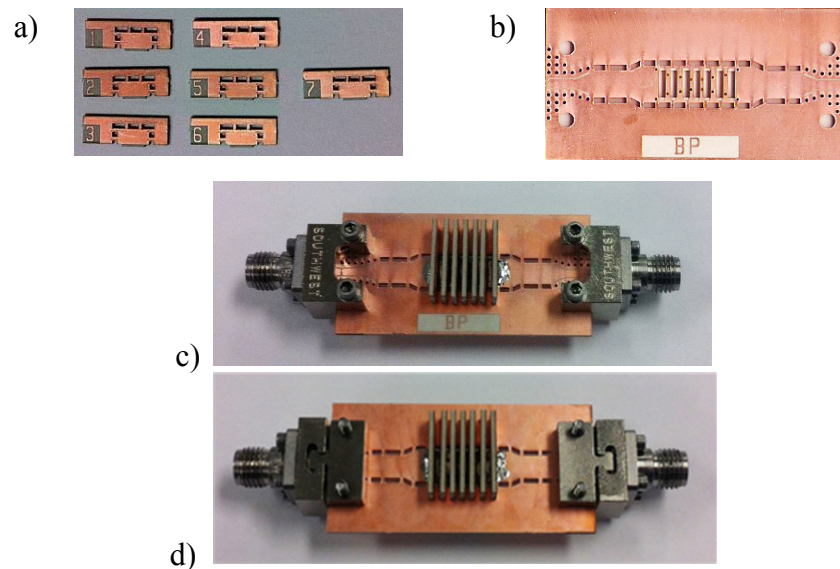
Filtre passe-bande fabriqué a) stubs terminés par des courts-circuits montés en surface, b) Vue de dessus du PCB principal avant assemblage, c) vue de dessus du filtre assemblé, d) Vue de dessous du filtre assemblé.
